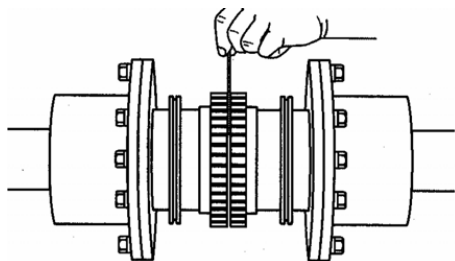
Ensemble moyeu d'arbre, joint d'étanchéité et moyeu d'écartement
